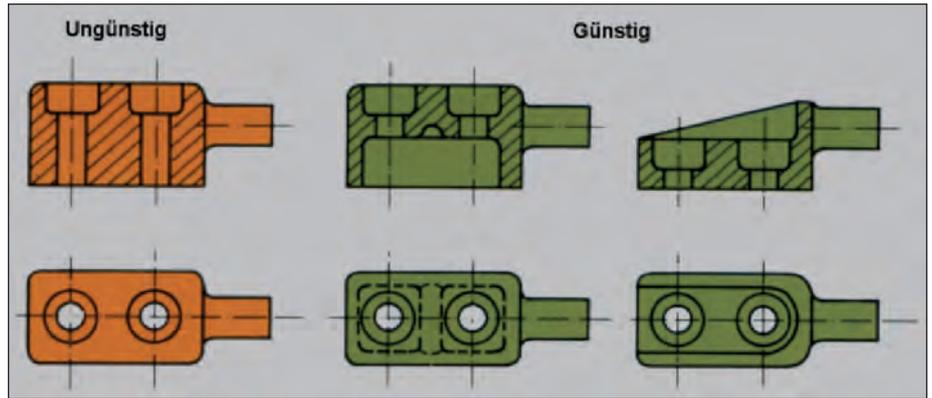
Gießtechnisch günstige Gestaltung eines Flansches
